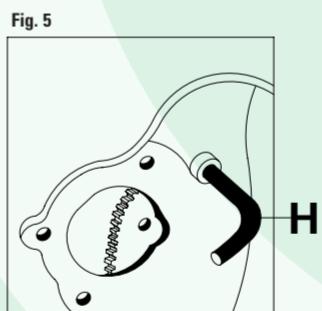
Insertar la herramienta de inmovilización del volante motor H.
